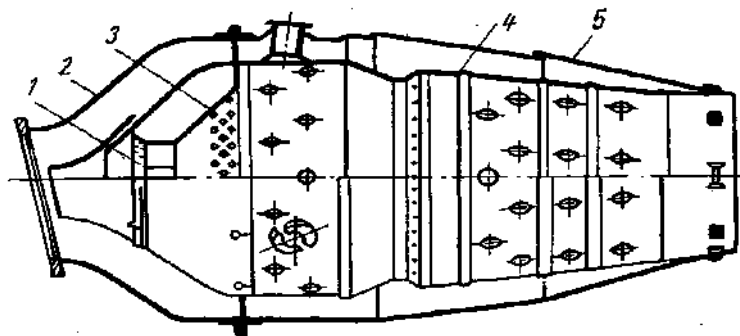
Конструкція трубчастої камери згоряння: 1 - завихритель; 2 - дифузор; 3 - фронтове пристрій; 4 - жаровая труба; 5 - корпус
